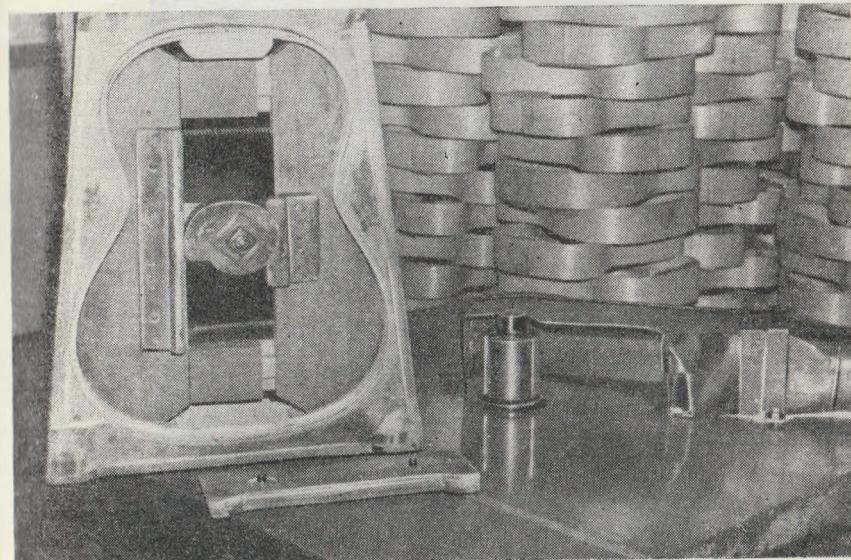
Застрожка кромок рамки корпуса гитары на фрезерном станке
